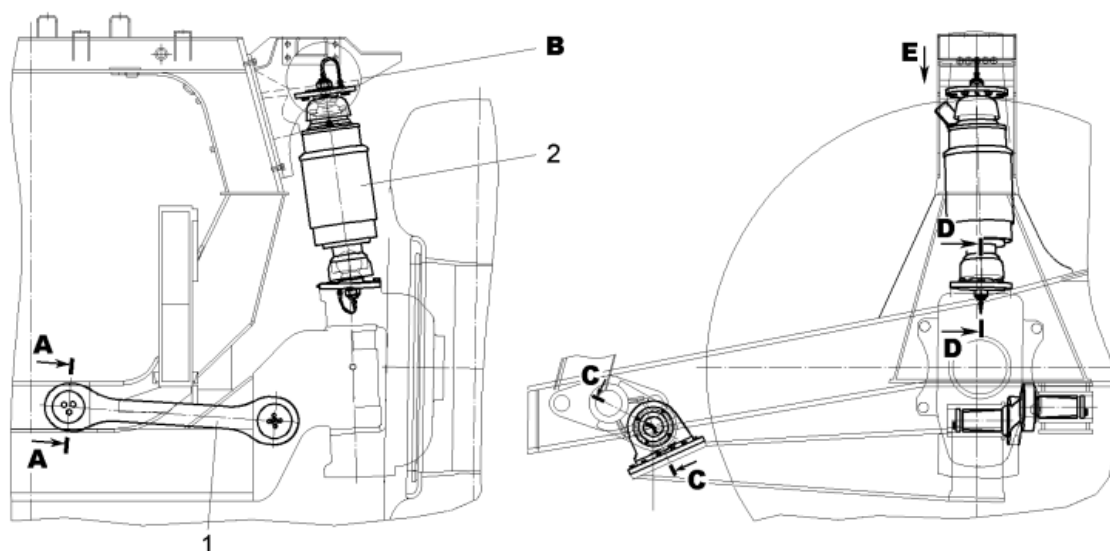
Передняя подвеска автосамосвала БЕЛАЗ-7513. 1 – штанга; 2 – пневмогидравлический цилиндр [56]
